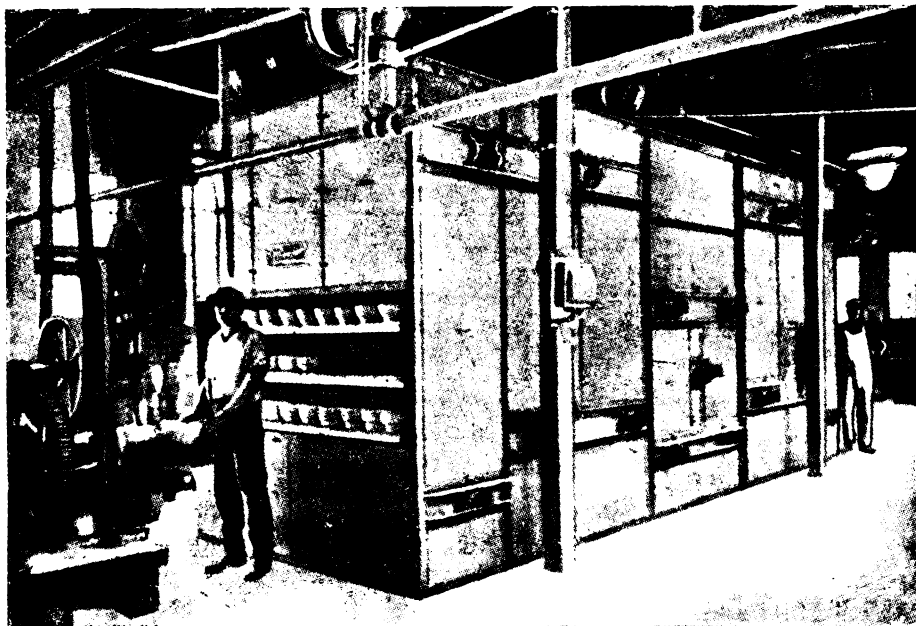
Конвейерная сушилка для изоляторов; рядом — горячий пресс для их формовки.
